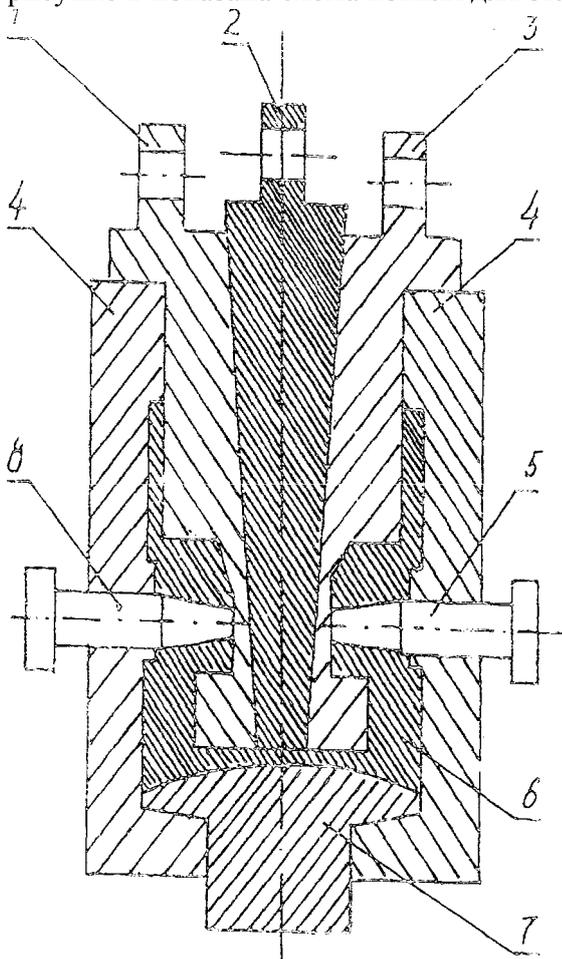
Кокиль для отливки с разъемным металлическим стержнем:
